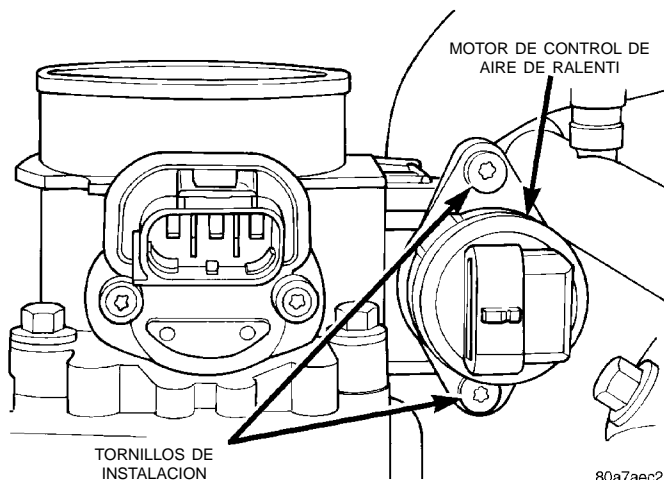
Pernos de instalación (Tornillos)—Motor de IAC —Motor de 4.0L
